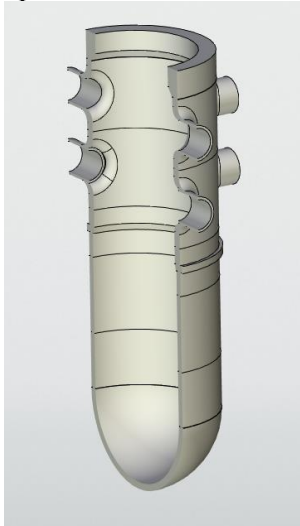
Модель корпуса реактора ВВЭР-1000 в разрезе
